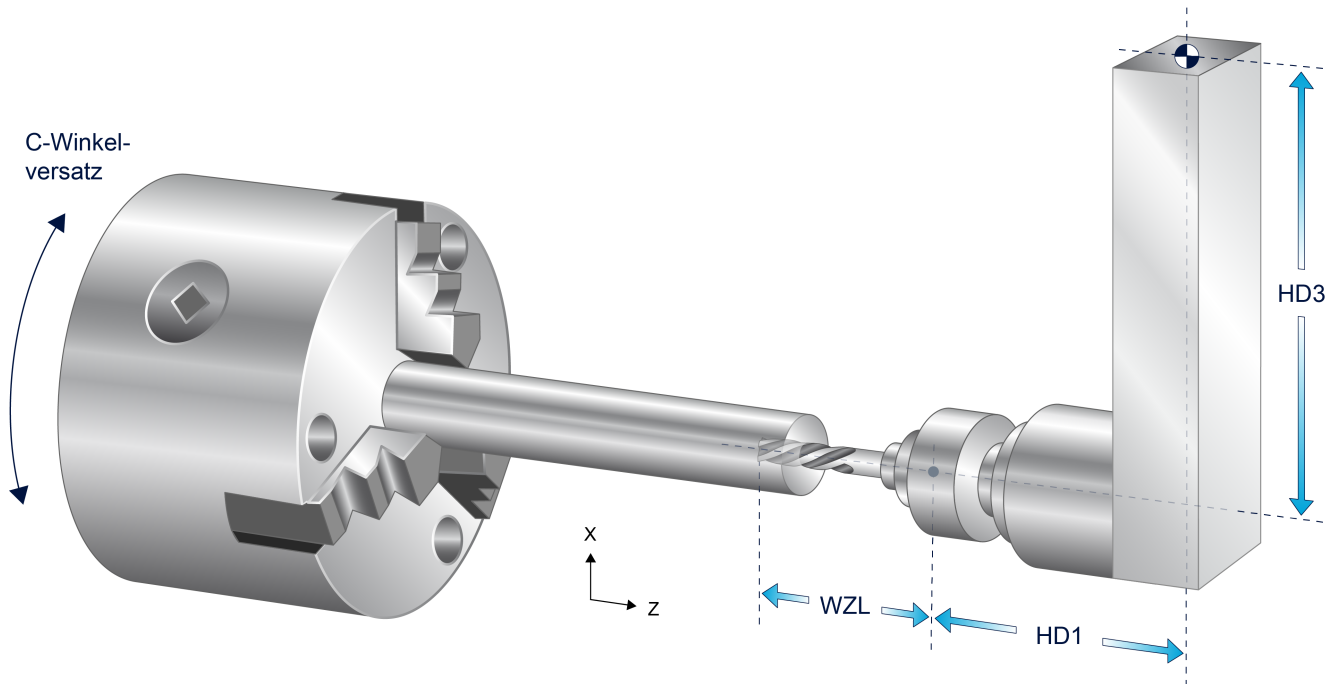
Werkzeugversätze für die Stirnflächenbearbeitung
